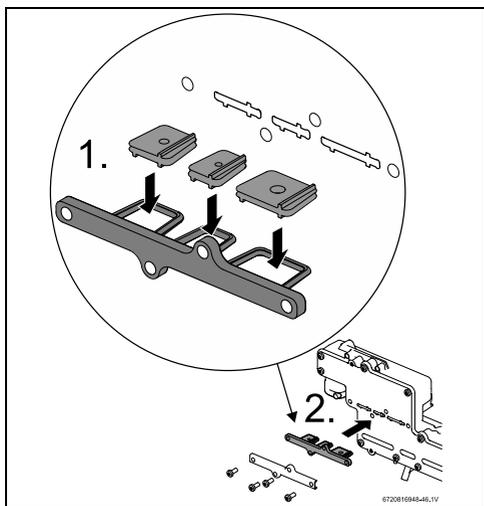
Assemblage de conversion de gaz pour l'appareil 160kBTU
